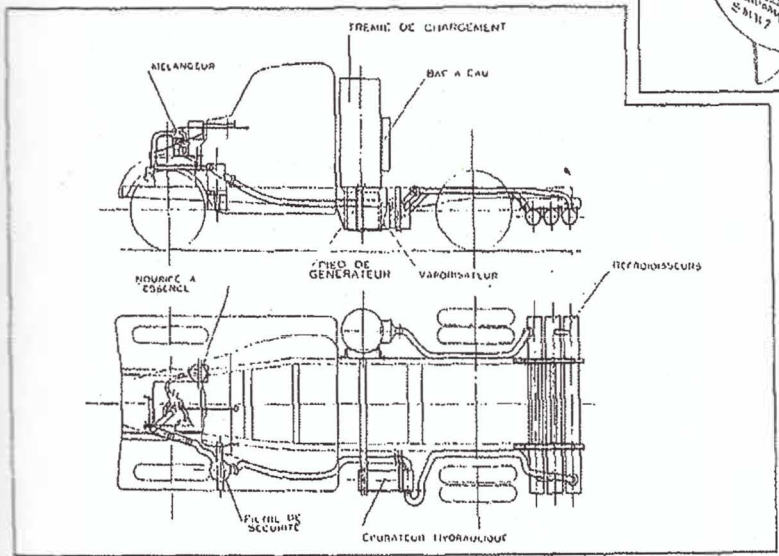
Equipement d'un Tracteur Chenard et Walker.
